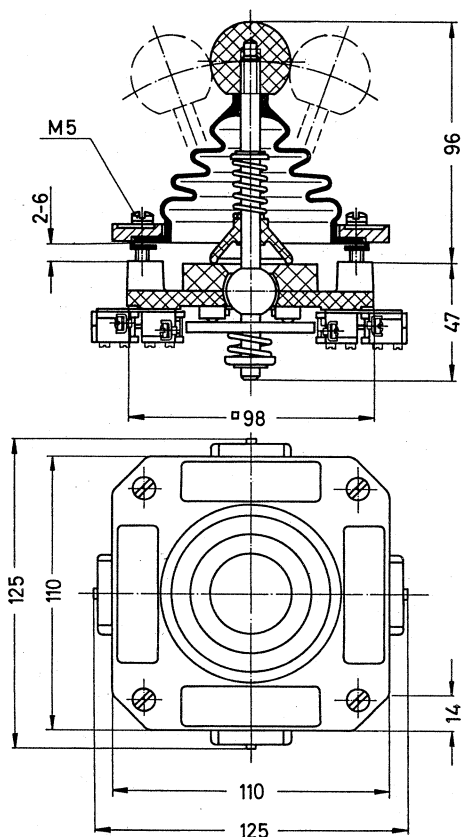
Universal-Steuerschalter, 1-stufige Ausführung mit Tandemanordnung der Schaltelemente, Typen HLU 110-11 bis HLU 110-14.
